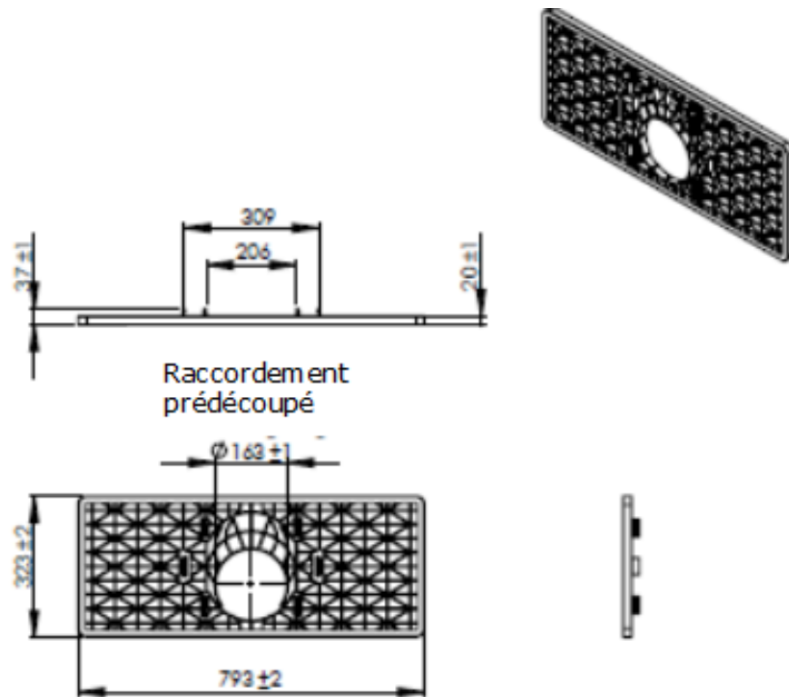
Plaque d'about et plaque d'about ajourée ouverture DN 150 ou DN 200 pour Rigofill inspect
